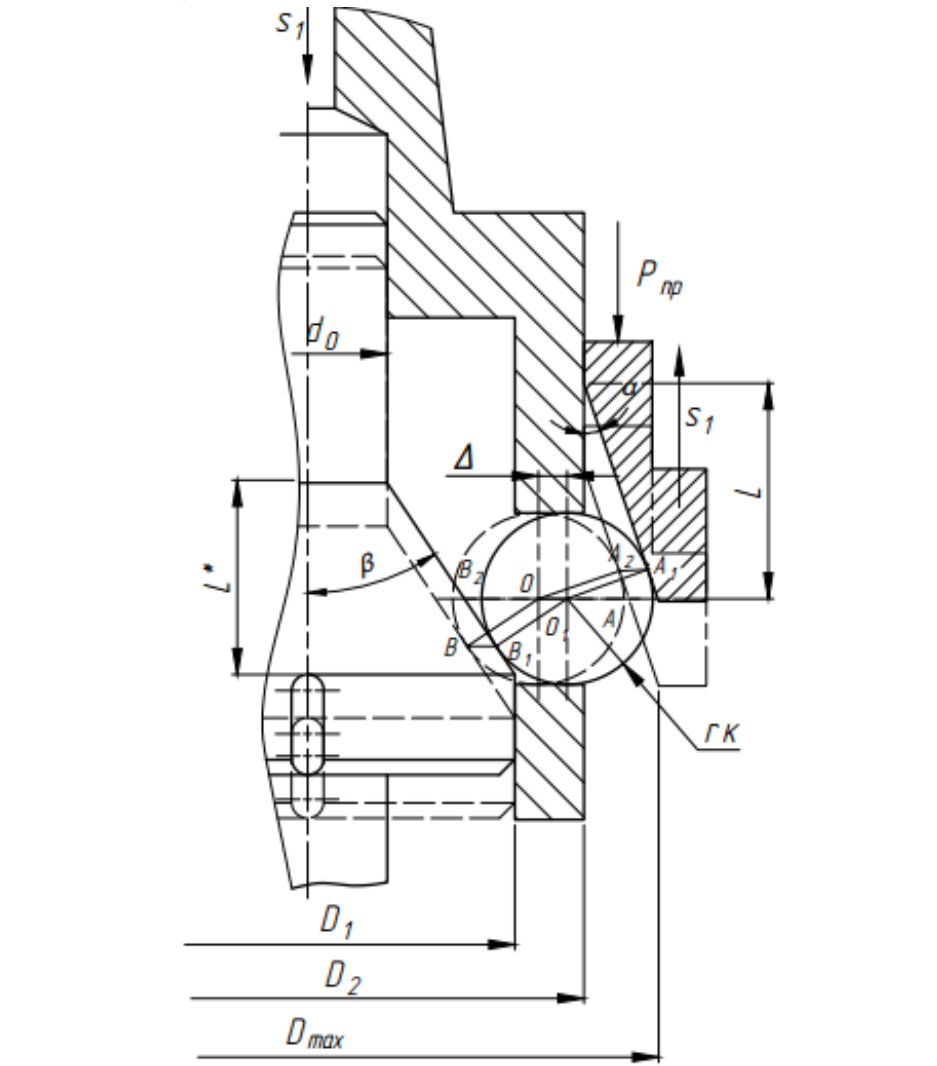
Розрахункова схема конусно-шарикового саморегульованого свердла
